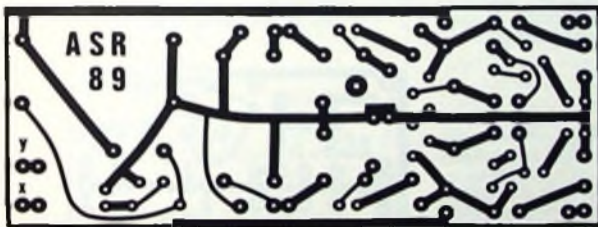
Printplatte des Aussteuerungsmessers für Netzbetrieb (Maßstab 1:2)
